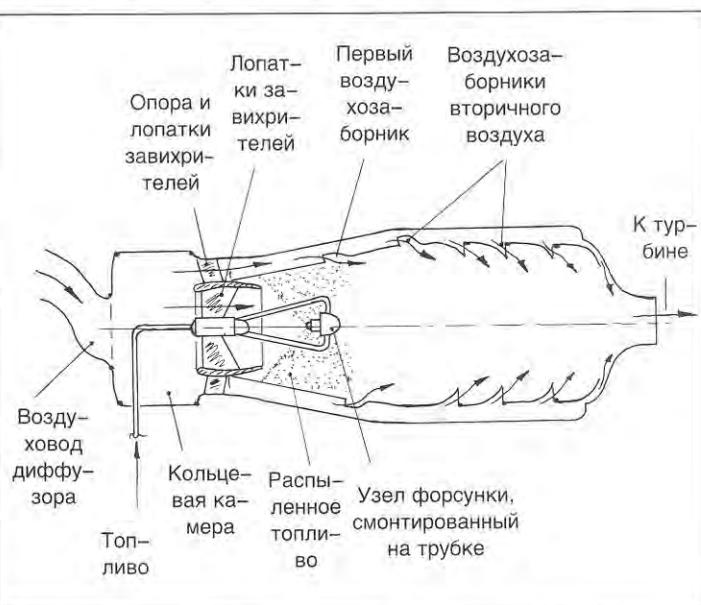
Эскиз камеры сгорания двигателя «Даймлер-Бенц» 109-007 (ZTL)
